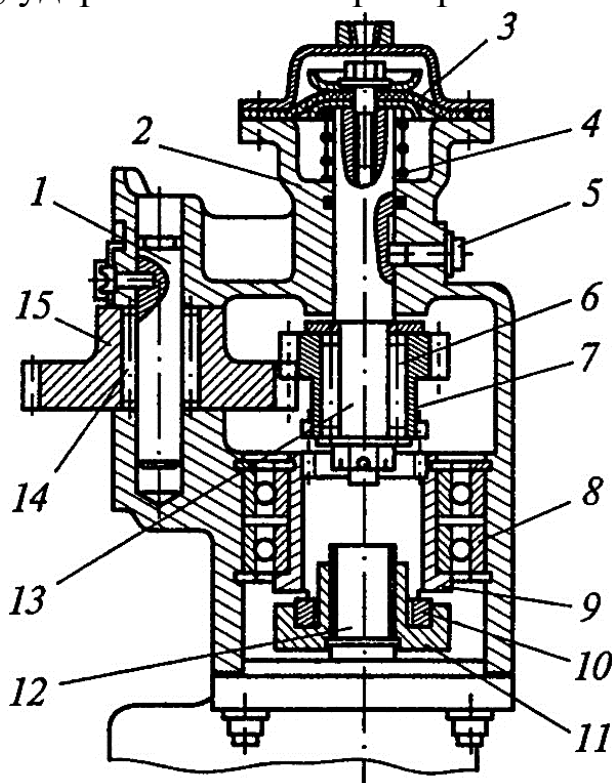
Коробка отбора мощности самосвалов КамАЗ: 1, 13 – оси; 2 – картер; 3 – диафрагма; 4 – пружина; 5 – винт; 6, 8, 14 – подшипники; 7, 15 – шестерни; 9 – полумуфта; 10 – призма; 11 – муфта; 12 – вал
